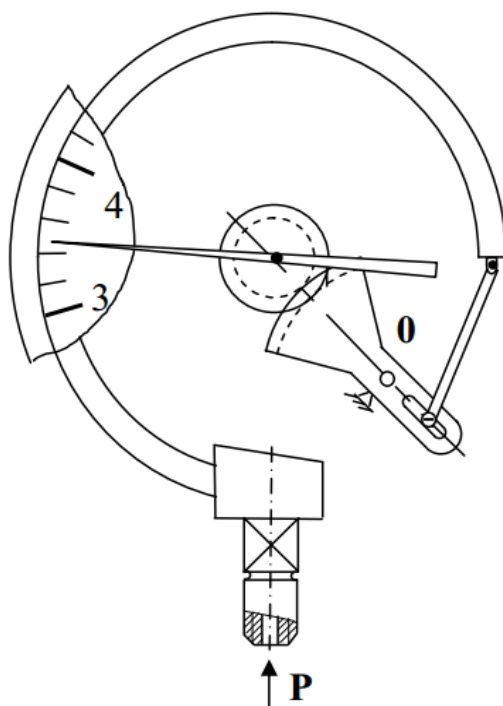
Конструкция манометра с одновитковой трубчатой пружиной
